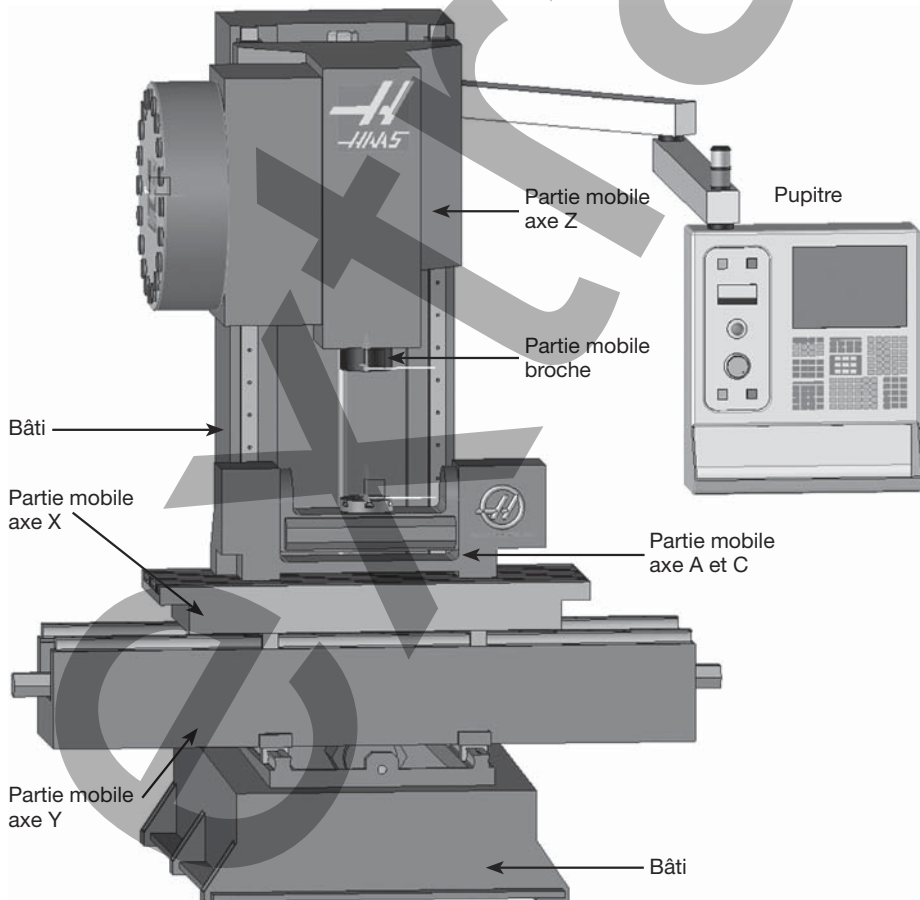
exemple de machine (centre d'usinage 5 axes VF4 sous TopSolid'Cam)
